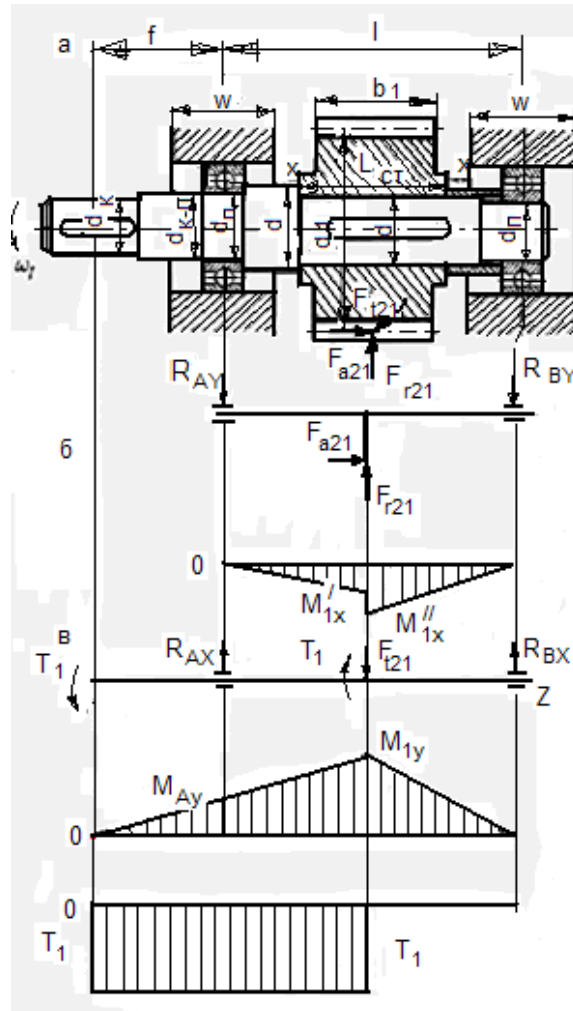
Схема ведучого вала циліндричного косозубого редуктора:
